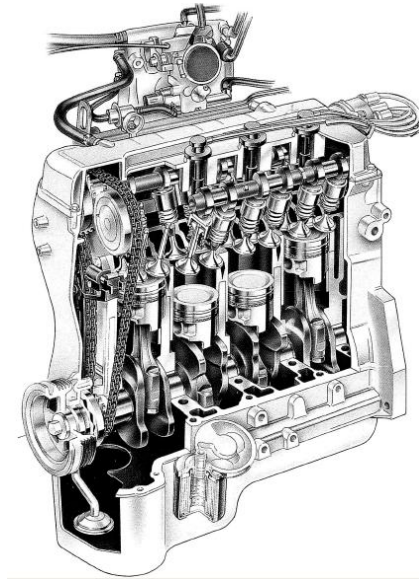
(Esquema en corte del motor K10A DOHC del Chevrolet Alto)
